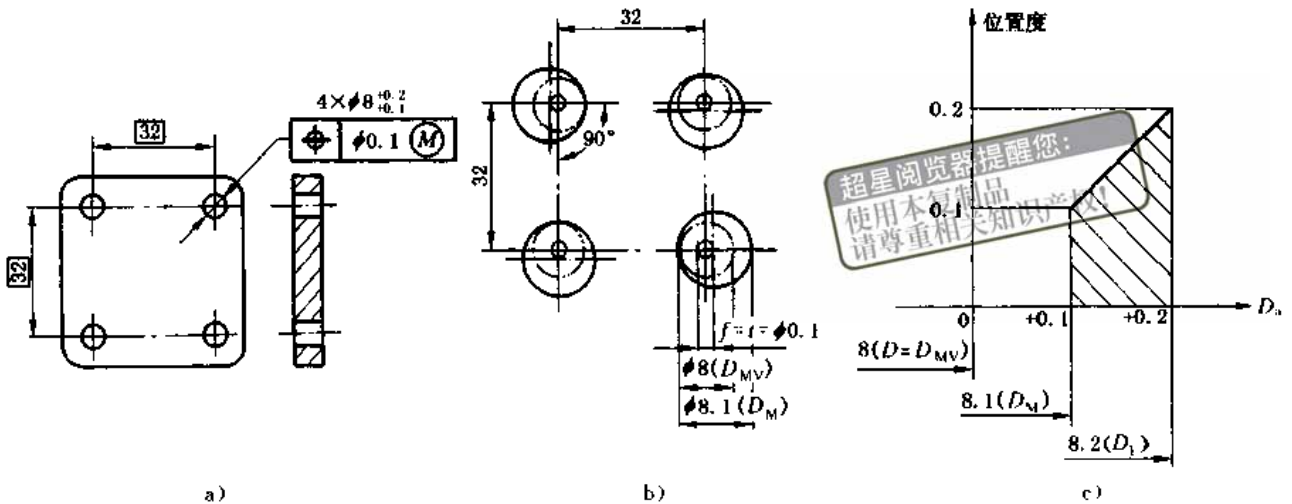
成组要素的位置度公差采用最大实体要求
